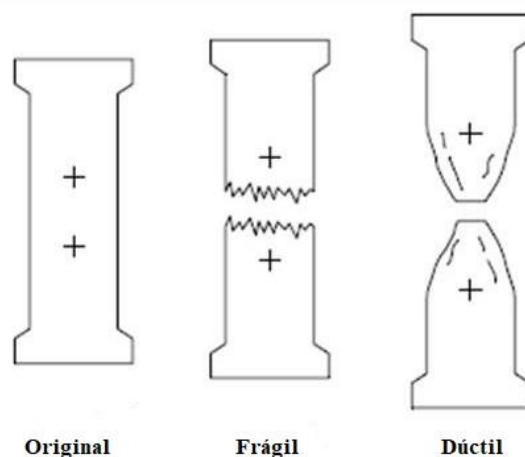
Ejemplo de fracturas frágil y dúctil desde el punto de vista macroscópico
